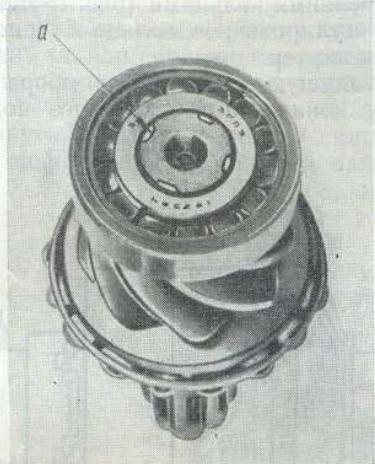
Раскерновка торца хвостовика после напрессовки подшипника:
